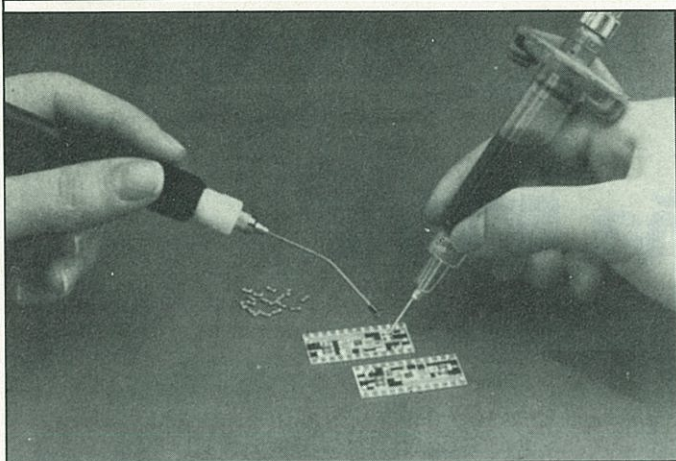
Montaje manual de un circuito impreso con soldadura de superficie.
